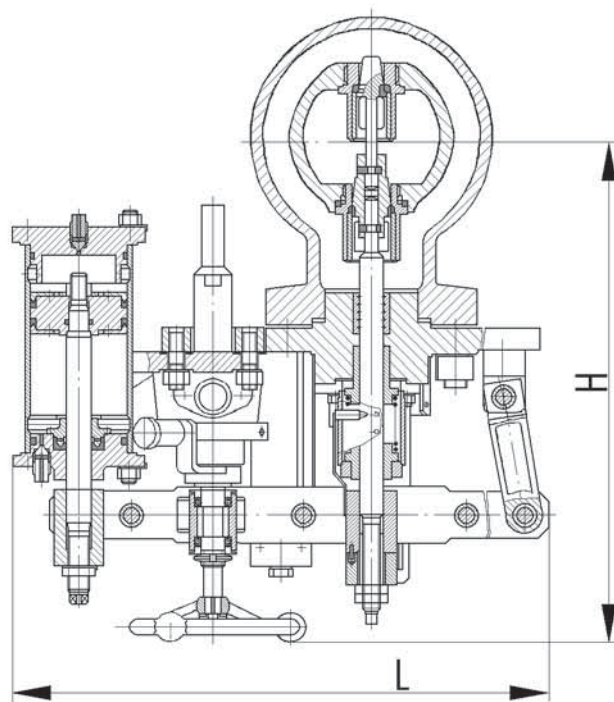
Клапан регулирующий проходной фланцевый с гидроприводом и ручным управлением
